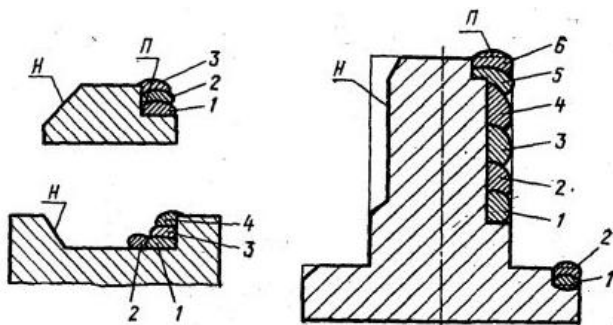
Правильная (П) и неправильная подготовка поверхностей под наплавку [48]:
